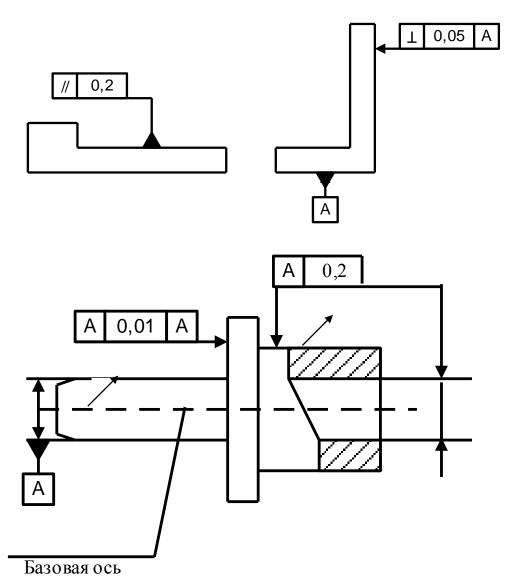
Обозначение базовой поверхности на чертеже детали при указании допусков на форму и расположение поверхностей
